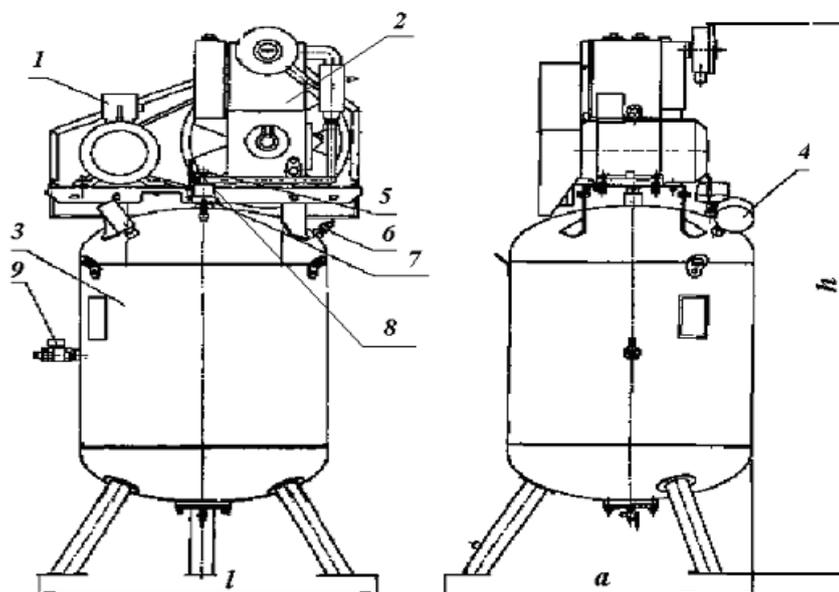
Установка компрессорная ЭПКУ с вертикальным расположением ресивера
